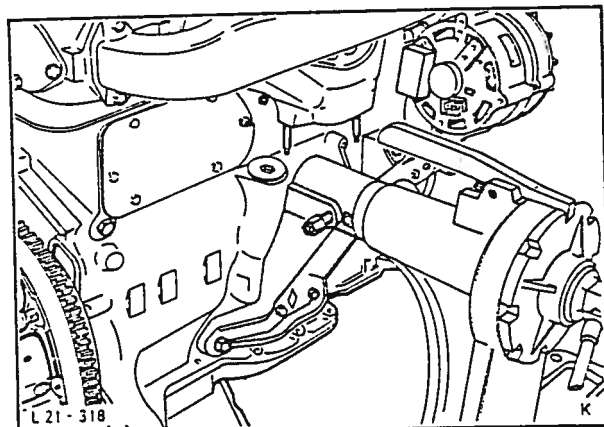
Monter motoren til stativet ved bruk av motorens festeanordning.
